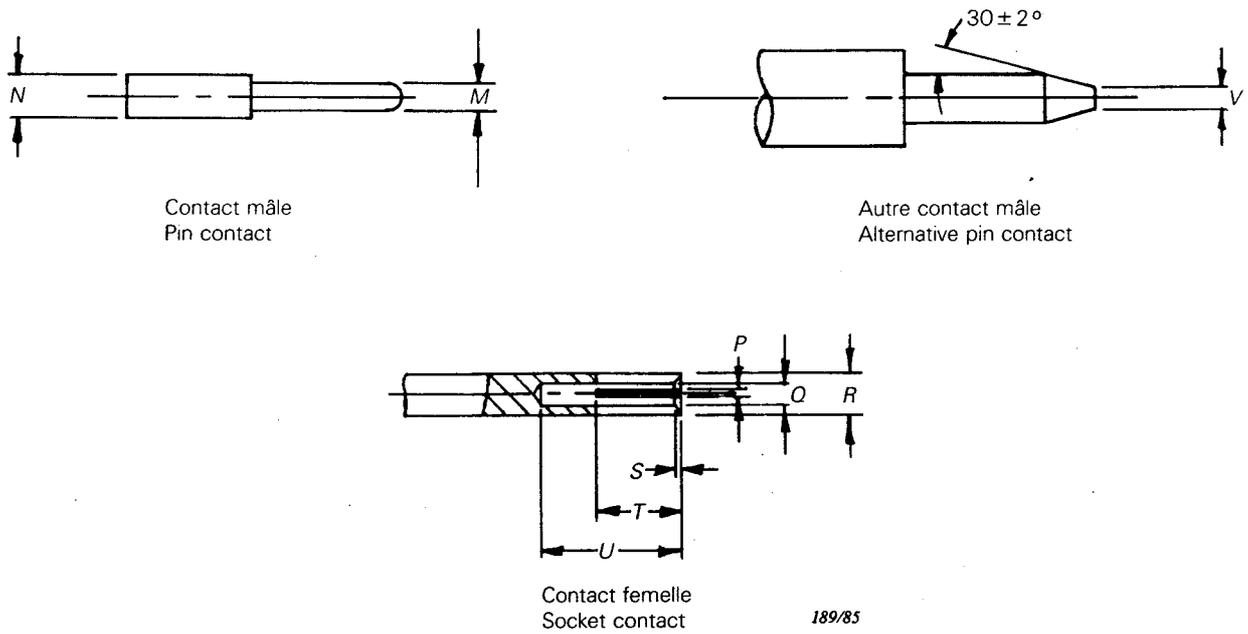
Contacts (pour les dimensions, voir le tableau).
